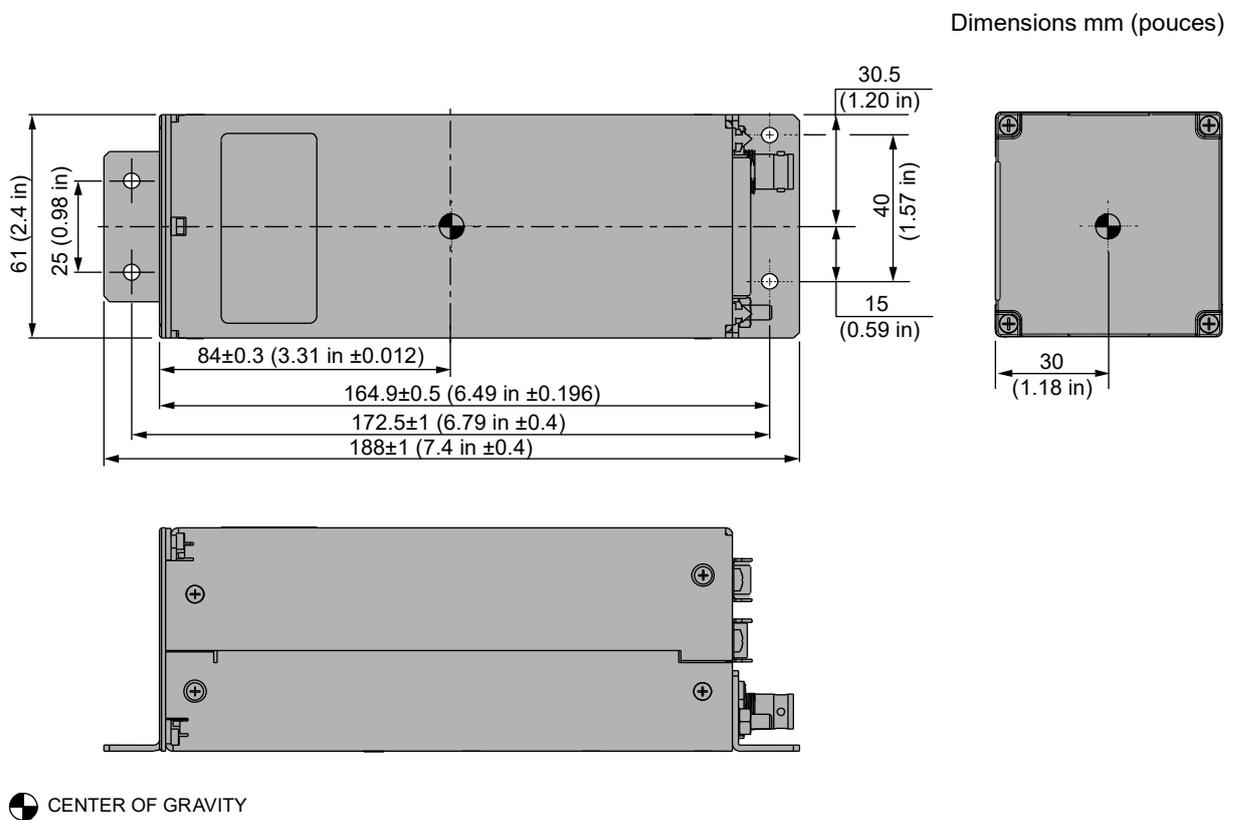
Vue du dessus, vue latérale RT6201
